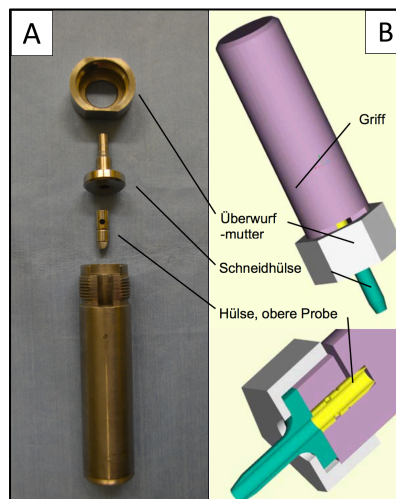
Das Entnahmewerkzeug für den Pin in seine Einzelteile zerlegt (A) und als Zusammenbau und im Schnitt in der CAD-Zeichnung; Abb. B aus [244]
